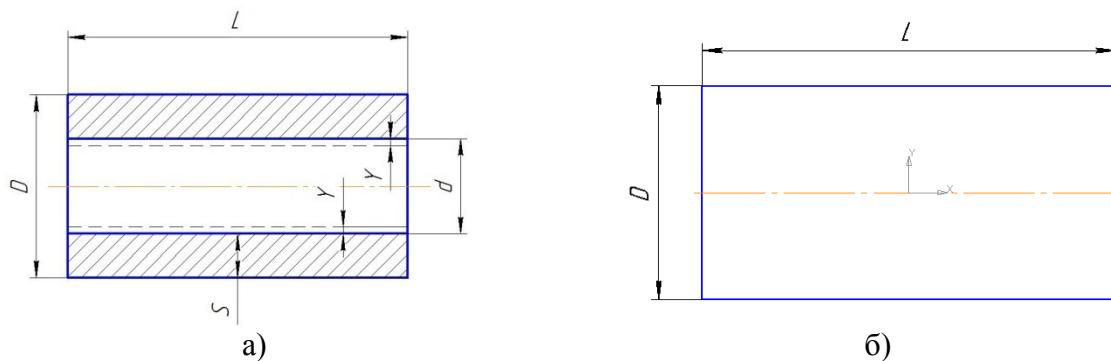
Цилиндрические детали (образцы) типа «втулка» (а) и «вал» (б),
